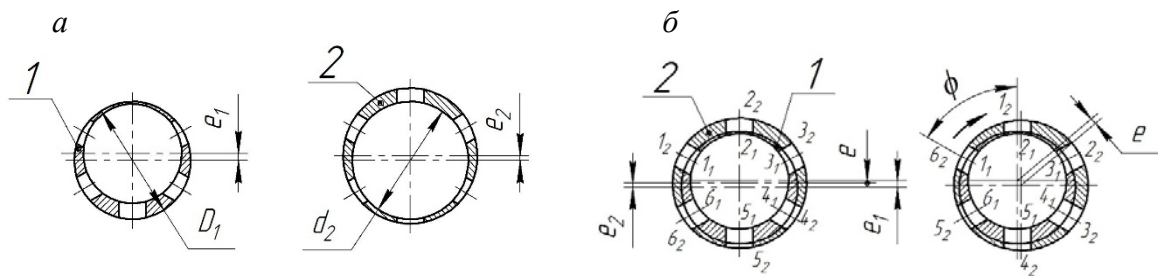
Конструкция эксцентричных втулок для настройки эксцентриситета установки резца
